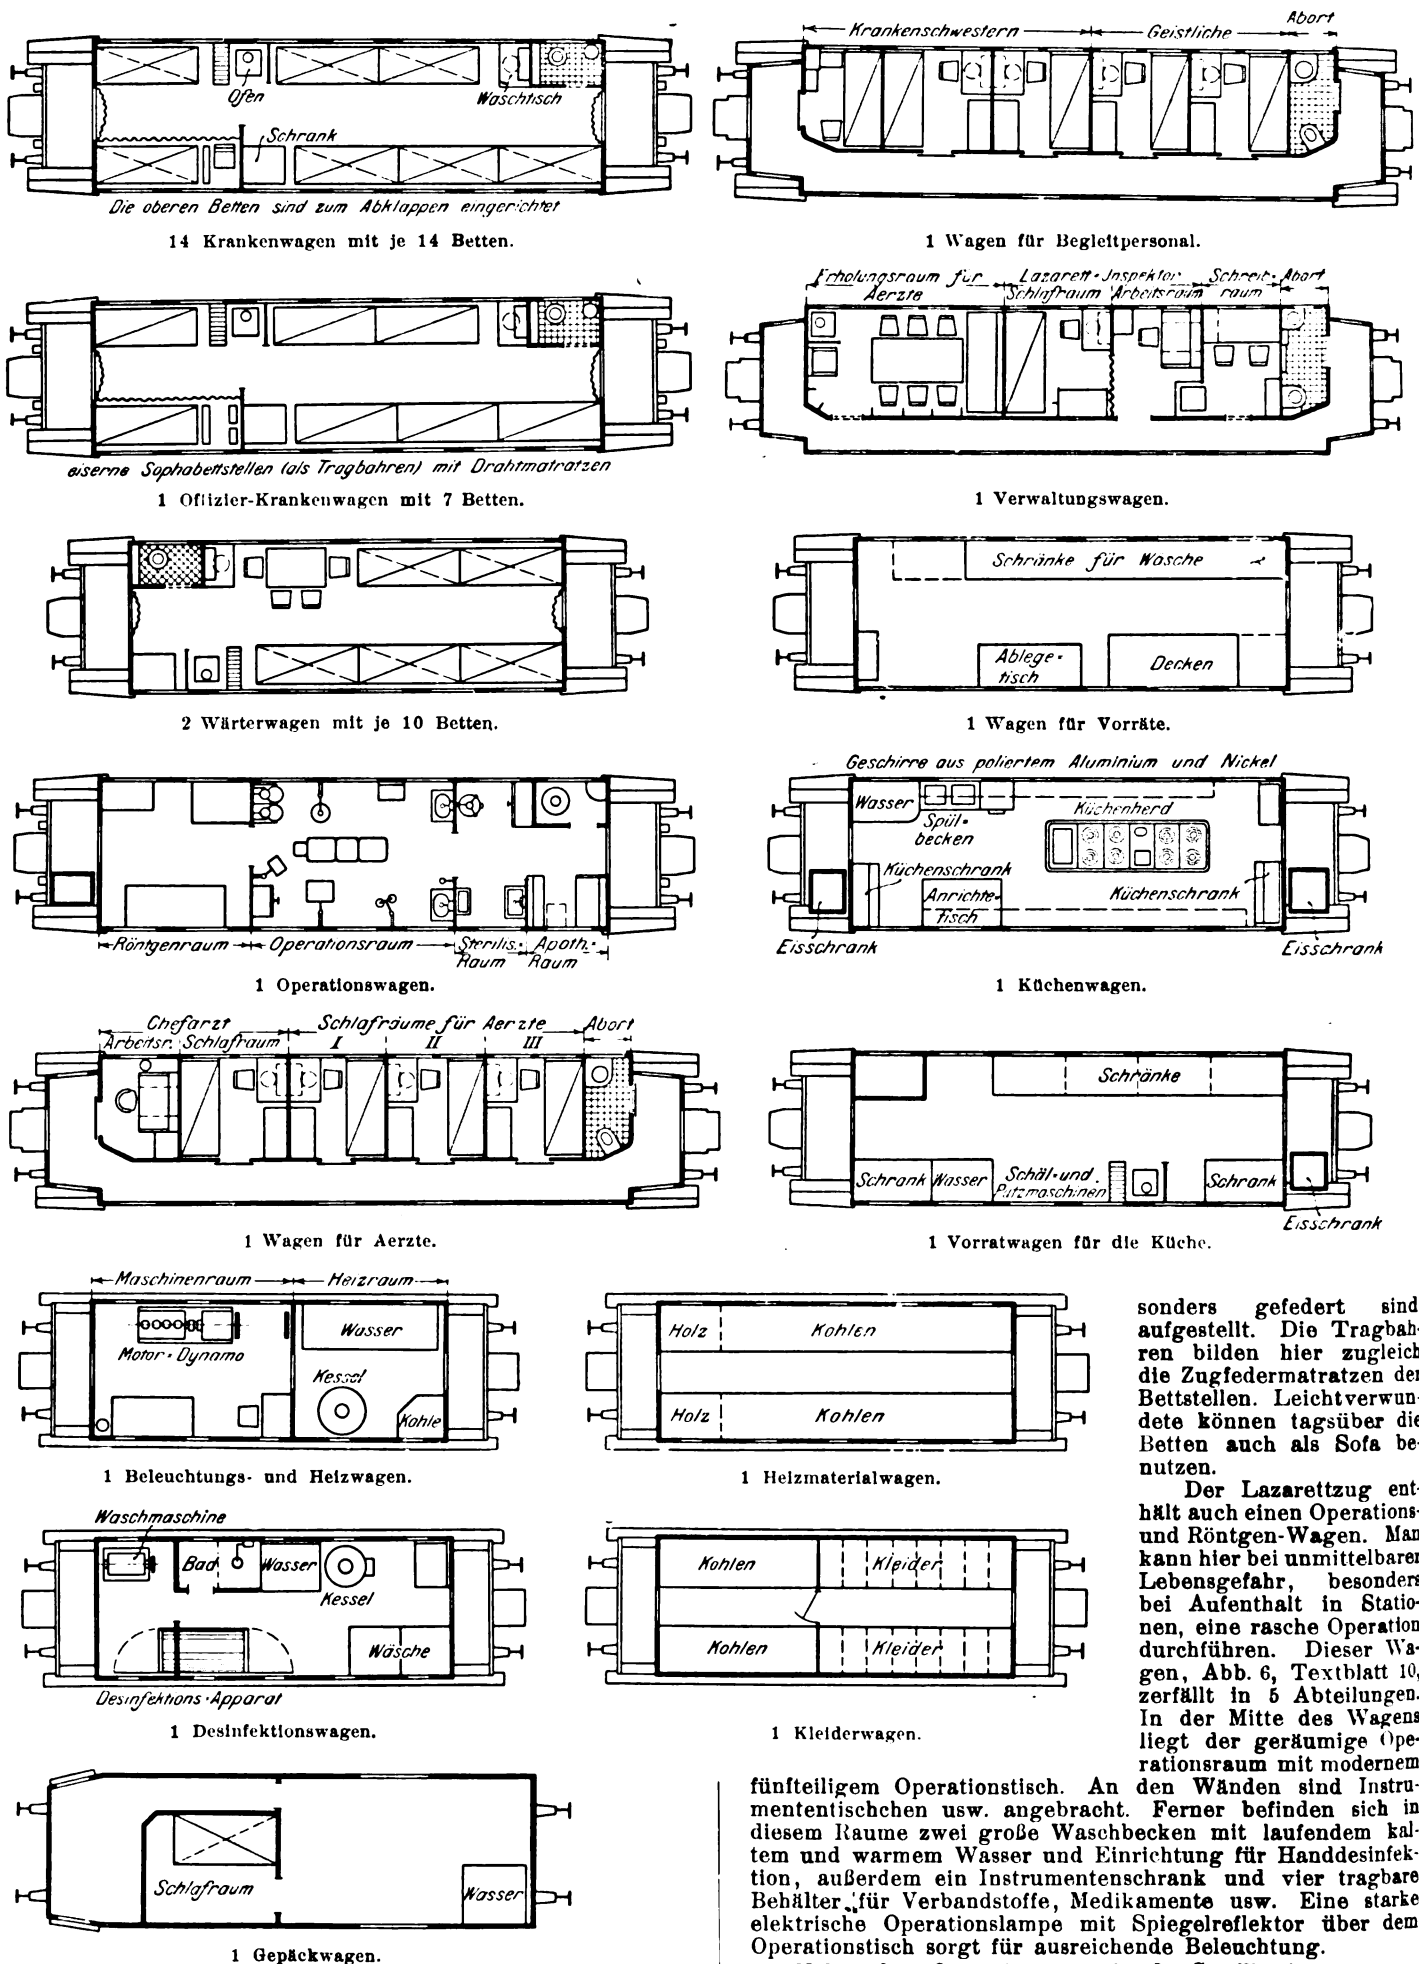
Grundrisse der Wagen des Lazarettzuges.
